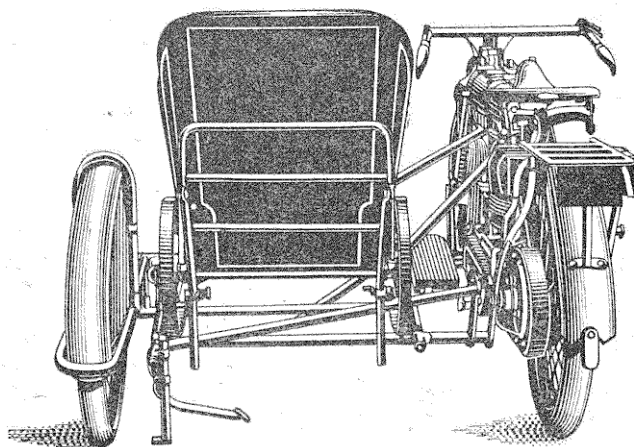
Sidecar sur moto B. A. T. vu de l'arrière pour laisser voir la disposition du châssis et des attaches au cadre de la motocyclette. (La roue du sidecar est montée sur cric.)
